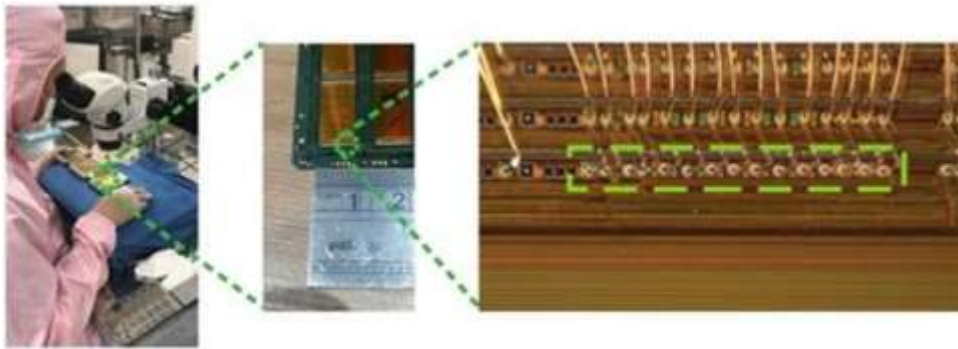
Inspeção visual convencional no processo de soldagem de pastilha de silício.
